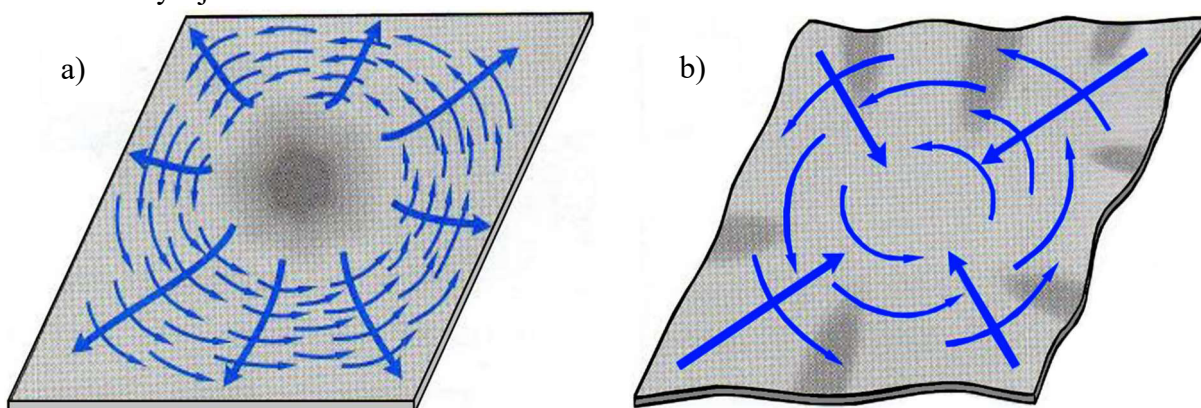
Průběh a pořadí úderů k napravení deformace [9]
